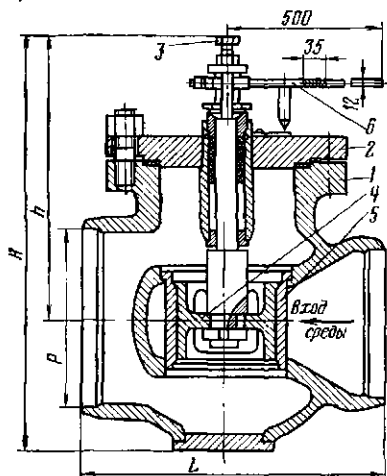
Клапан регулирующий поворотный  $D_y$  50, 80, 100, 150, 200, 250 и 300 мм.
